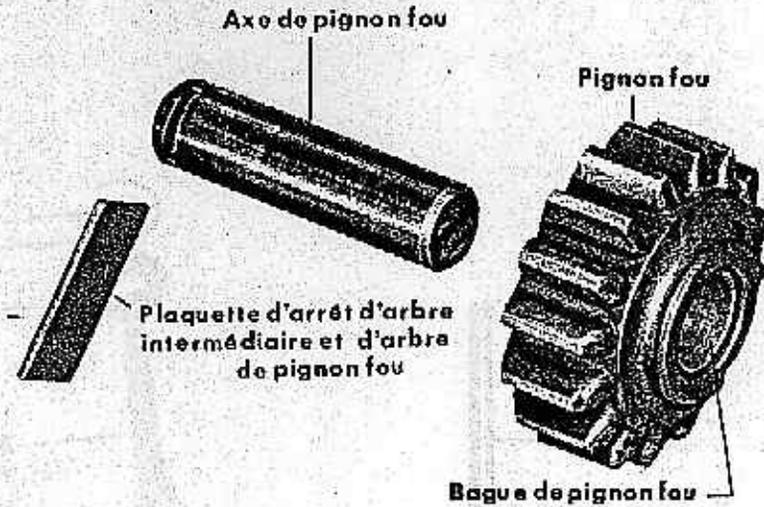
Ensemble du pignon fou. Vue éclatée.
